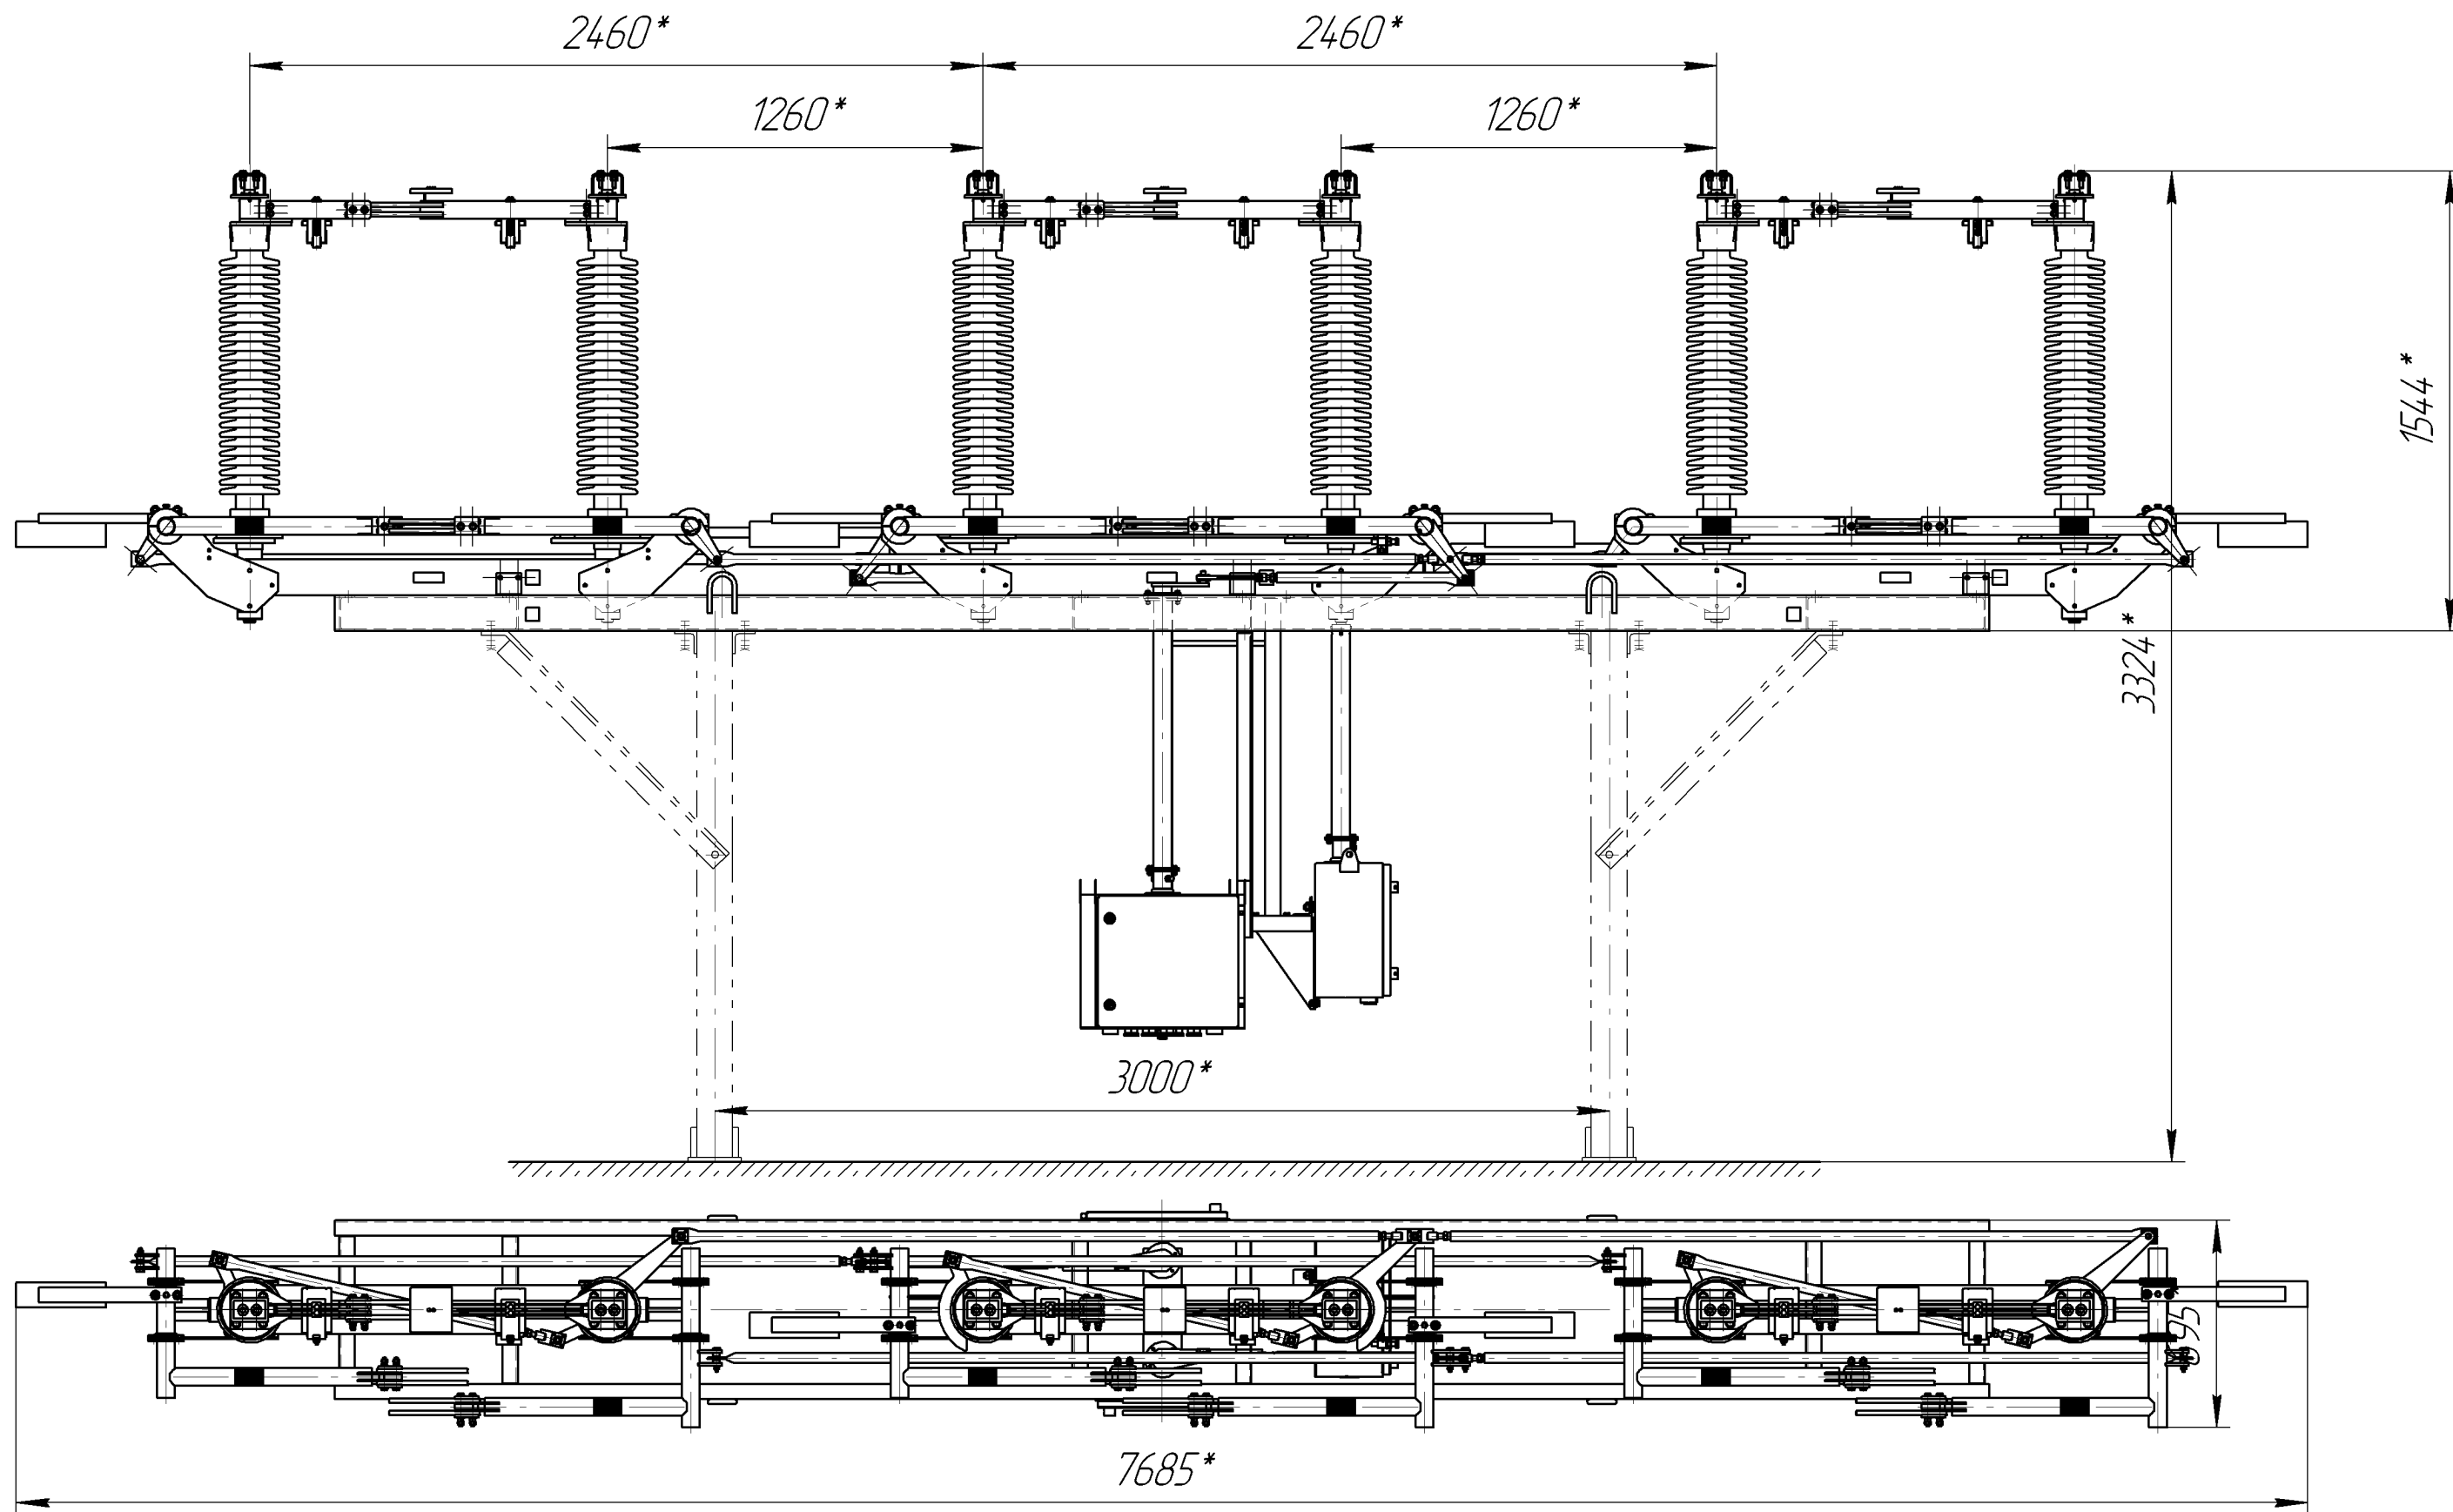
Разъединитель трёхполюсный РГП СЭЩ - 110 килевого исполнения
